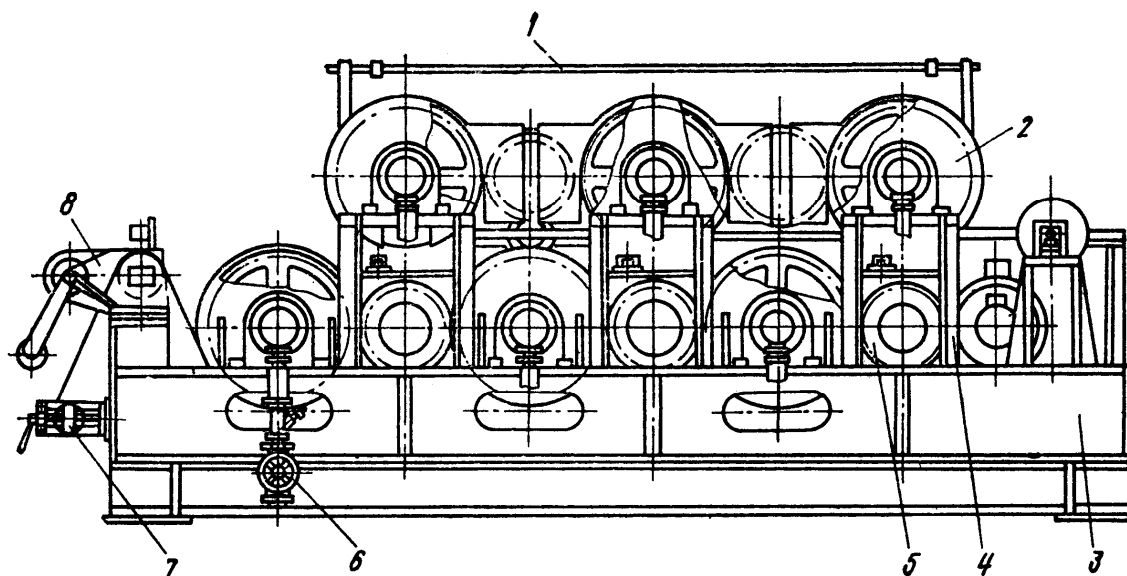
Схема охолоджувального пристрою барабанного типу: 1 – аварійний вимикач тросового типу; 2 – барабан; 3 – рама; 4 – стійки; 5 – зубчаста передача; 6 – вентиль; 7 – натяжний пристрій; 8 – селісинний датчик
